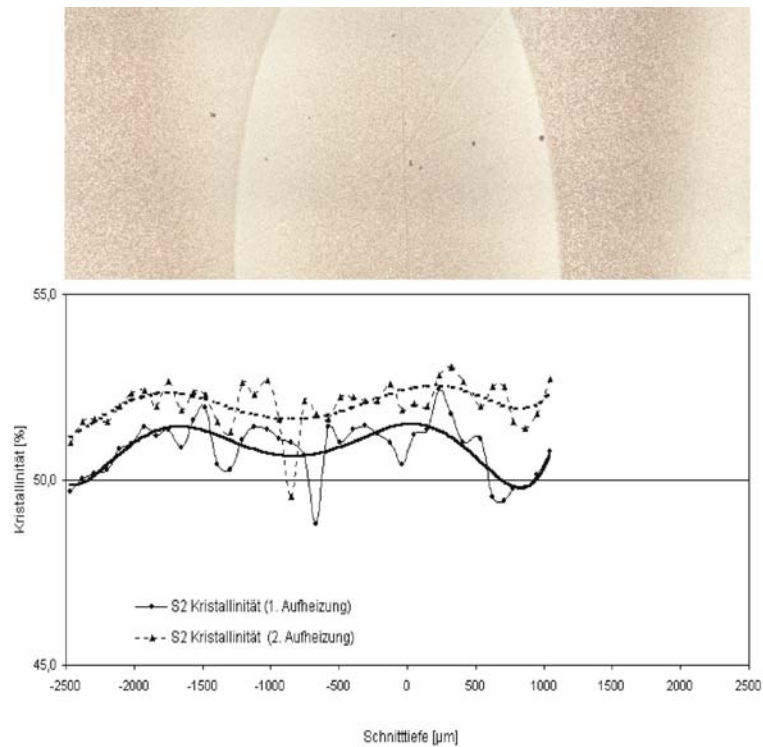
Kristallinität nach 1. und 2. Aufheizung im Querschnitt einer der Schweißnahtserie S2 entnommenen Probe mit bildhafter Zuordnung zum geätzten Querschnitt der Schweißnaht.
